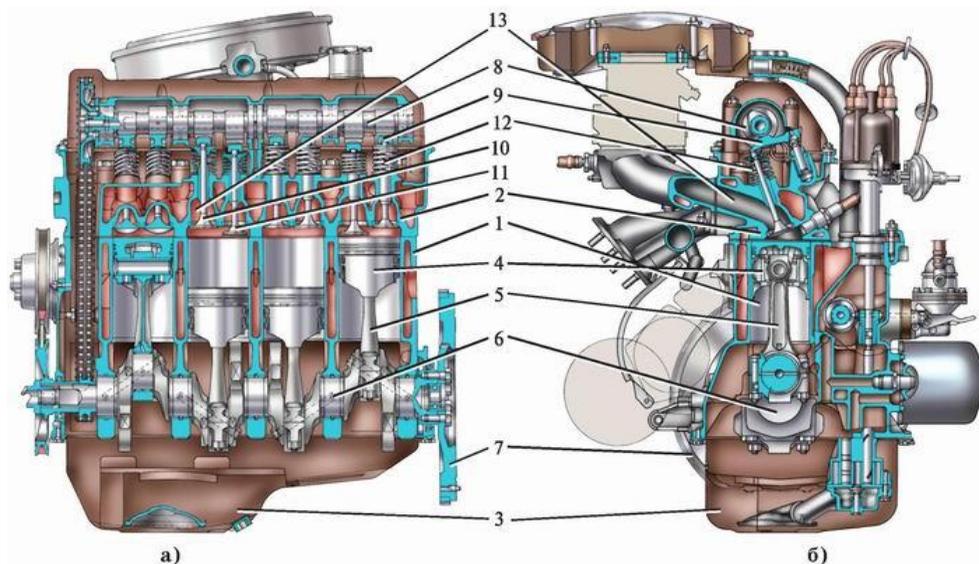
Основные детали четырехцилиндрового бензинового двигателя: а) продольный разрез; б) поперечный разрез; 1 – блок цилиндров; 2 – головка блока цилиндров; 3 – поддон картера; 4 – поршни с кольцами и пальцами; 5 – шатуны; 6 – коленчатый вал; 7 – маховик; 8 – распределительный вал; 9 – рычаги; 10 – впускные клапаны; 11 – выпускные клапаны; 12 – пружины клапанов; 13 – впускные и выпускные каналы
